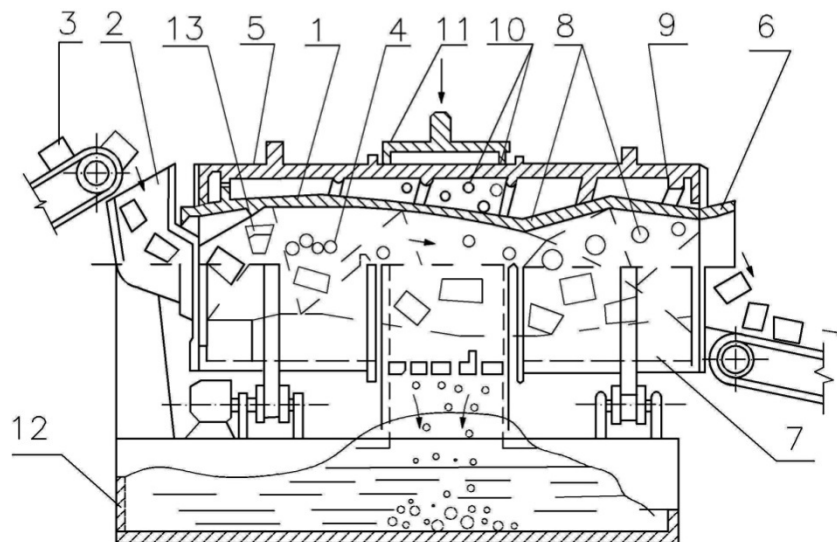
Станок для непрерывной отделочно-зачистной и упрочняющей обработки деталей: 1 - винтовой ротор; 2 - загрузочное приспособление; 3 - обрабатываемые детали; 4 - шарики; 5 - наружный барабан; 6 - выходной люк; 7 - отходы обработки; 8 - отверстия для вывода отходов обработки; 9 - винтовые направляющие; 10 - отверстия диаметром меньше гранул рабочей среды; 11 - кожух; 12 - отстойная камера; 13 - средство для перегрузки
